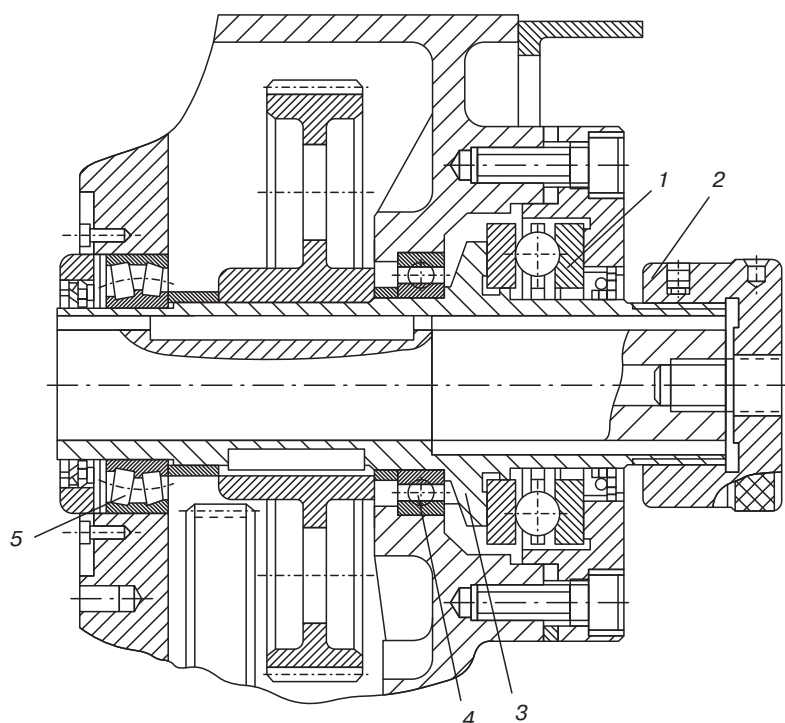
Схема узла подшипников одношнекового экструдера с шариковым упорным подшипником
